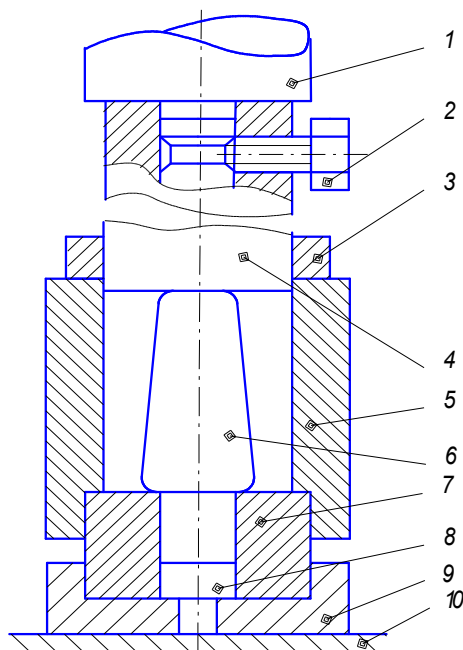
Приспособление для окончательной высадки-формовки (исходное положение):
